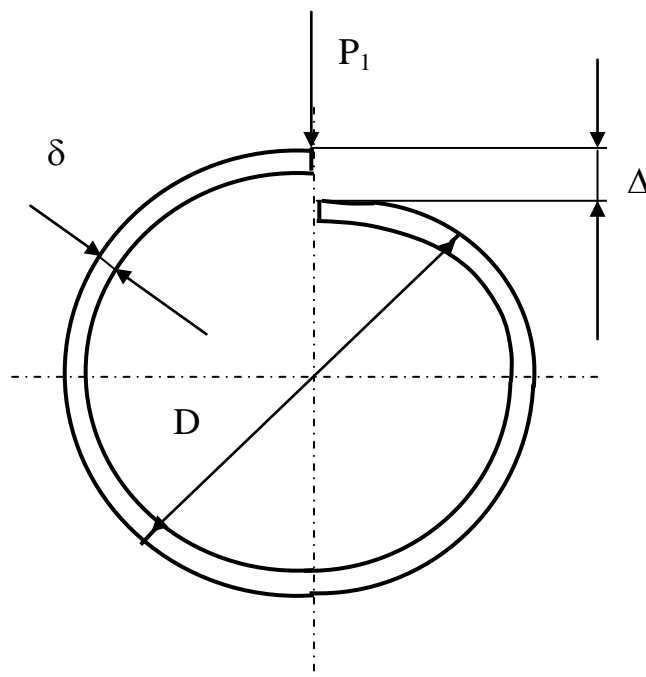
Розрахункова схема визначення величини сили для усунення зміщення кромки циліндричної обичайки
